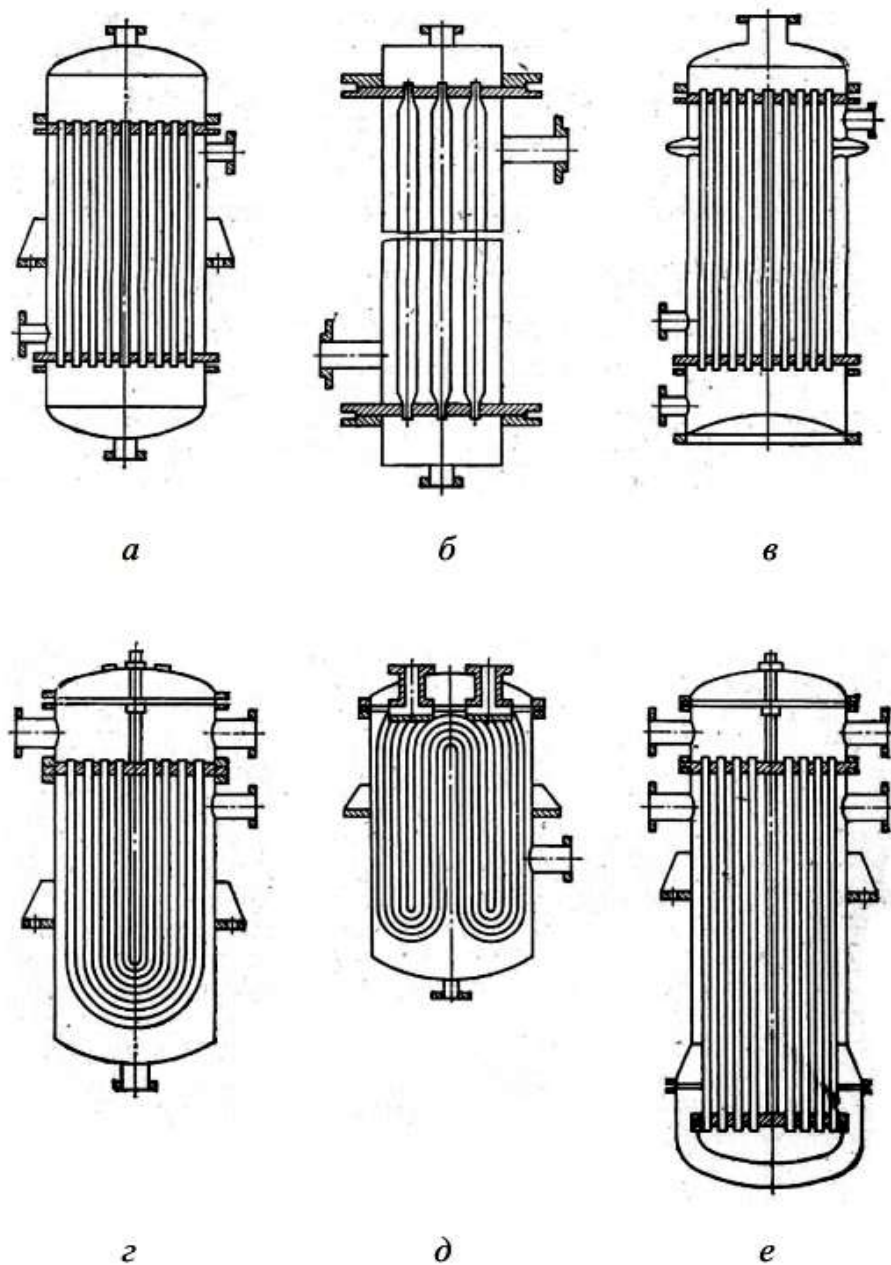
Кожухотрубчатые рекуперативные теплообменные аппараты: а, б — с жестким креплением труб в трубных решетках; в — с линзовыми компенсаторам корпусе; г, д — с U- и W-образными трубками; е — с нижней плавающей распределительной камерой [61]
